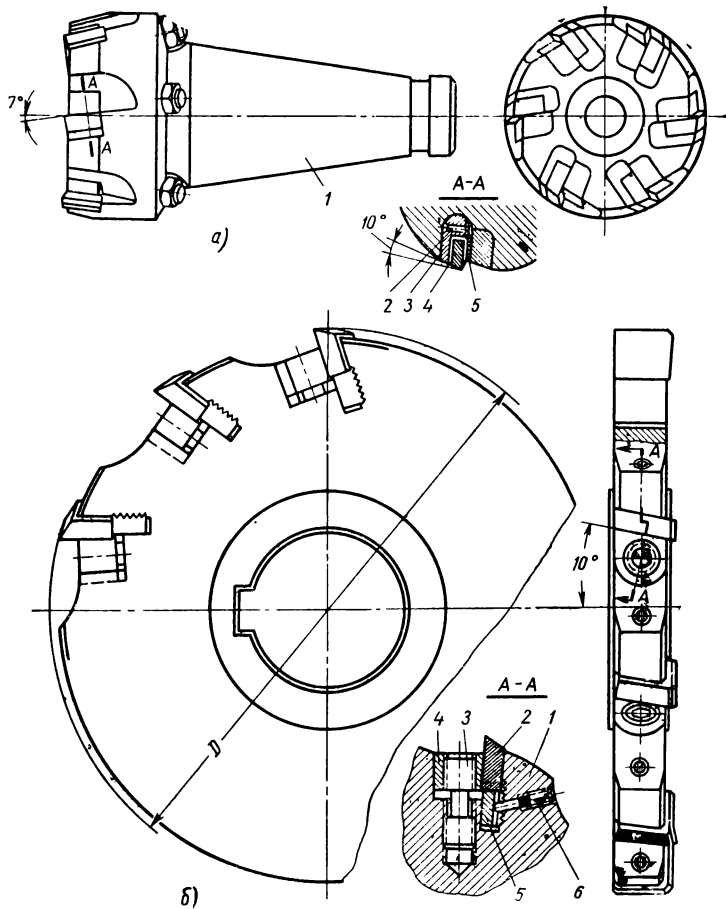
Фрезы с механическим креплением минералокерамических пластинок:
